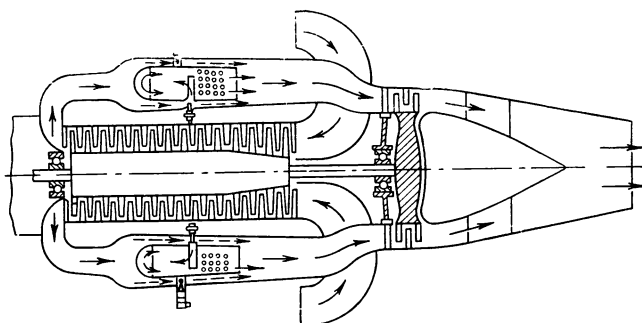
Схема ТВД с петлевым движением воздуха и индивидуальными камерами сгорания, расположенными вокруг компрессора
